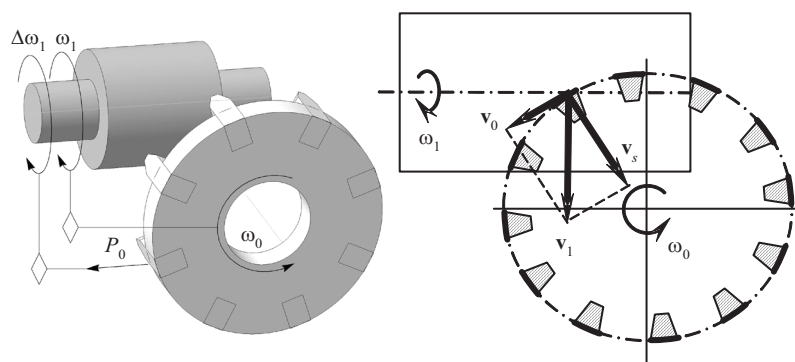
Схема нарезания червяка цилиндрической резцовой головкой
